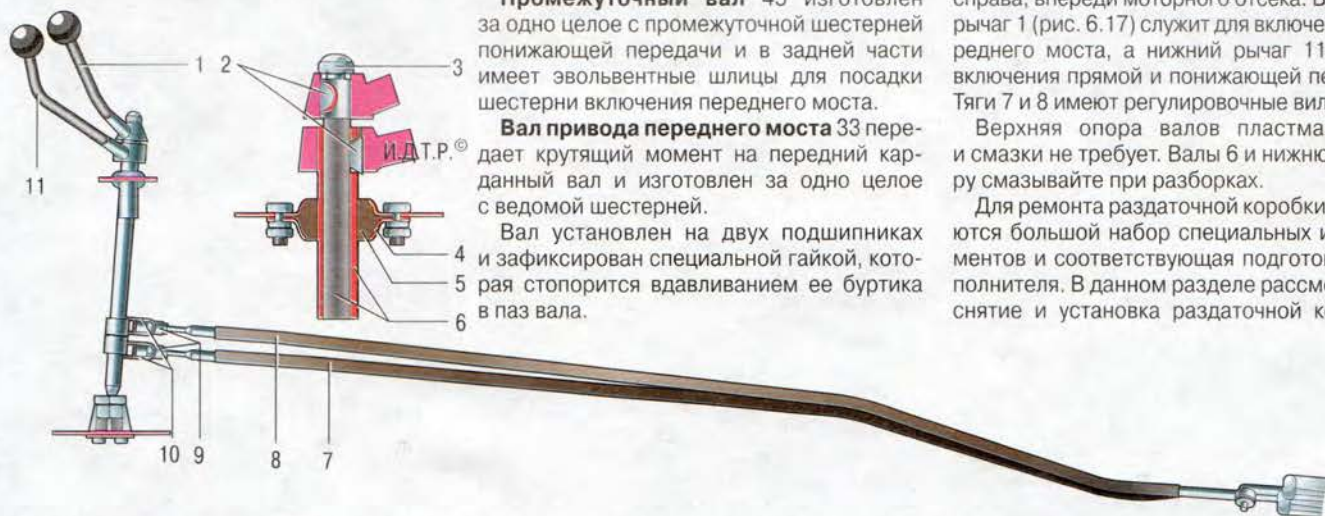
Механизм управления раздаточной коробкой: 1 – рычаг включения переднего моста; 2 – шпонки; 3 – гайка; 4 – шарнирный подшипник; 5 – корпус подшипника; 6 – валы переключения; 7 – тяга включения переднего моста; 8 – тяга включения прямой и понижающей передач; 9 – контргайки; 10 – регулировочные вилки; 11 – рычаг включения прямой и понижающей передач
